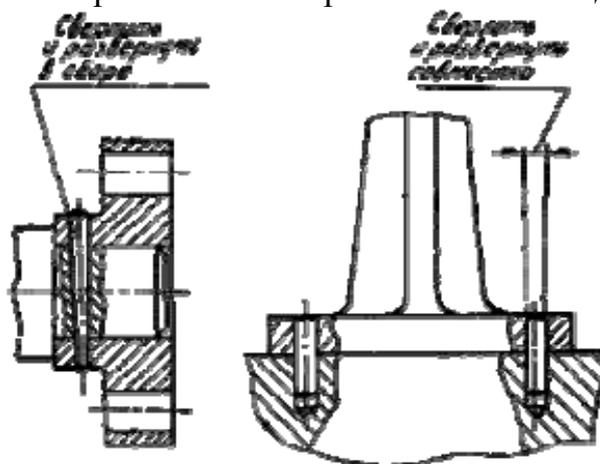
Сборочные единицы, нуждающиеся в обработке отверстий в процессе сборки
